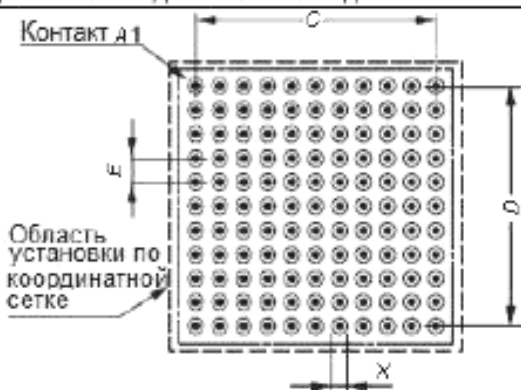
Размеры посадочного места для корпуса BGA (квадратного)
